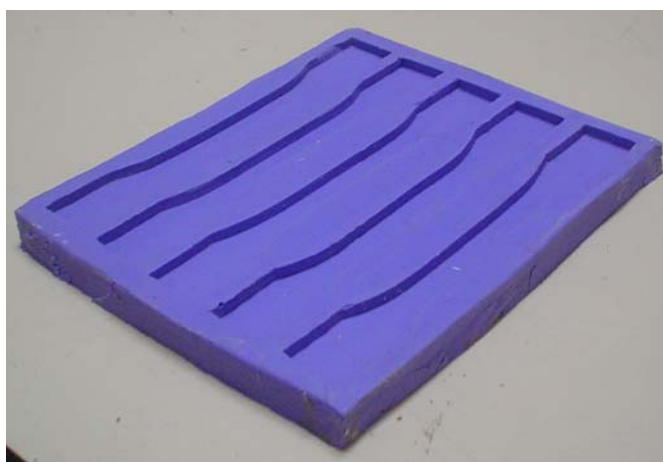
Molde em silicone para moldagem de corpos de prova de tração.
